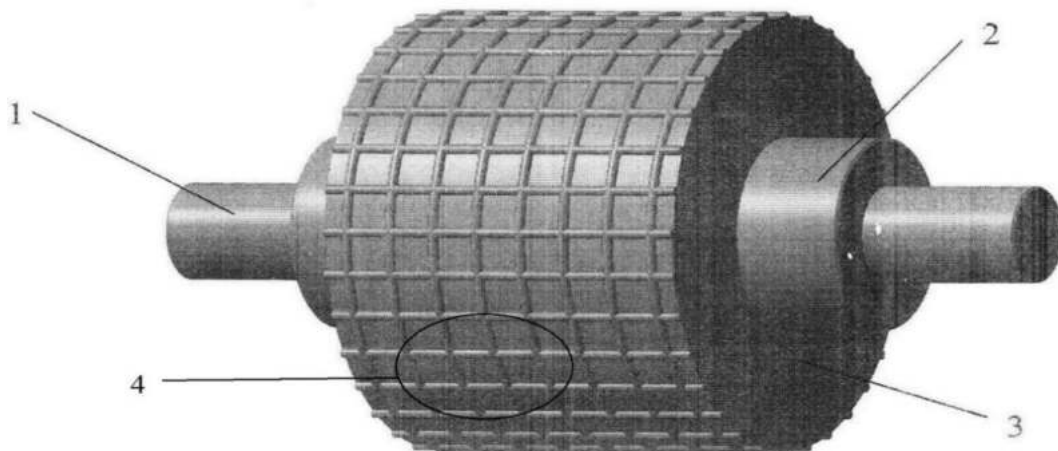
Валок четырёхвалковой дробилки [3]:
